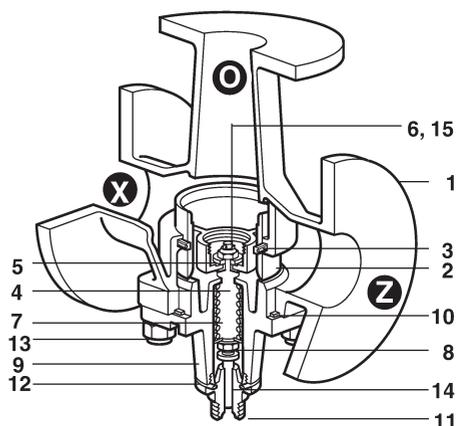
Valvola con attacchi flangiati DN50, 80 e 100
